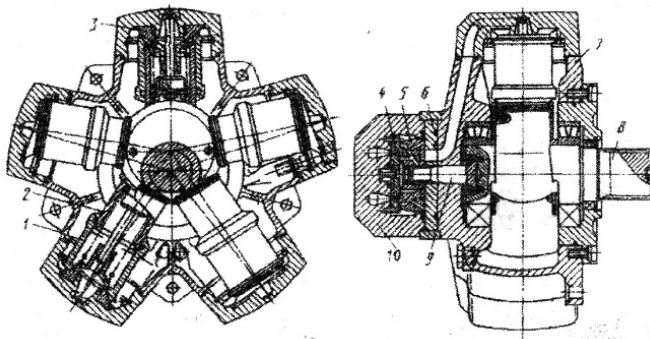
Высокомоментный радиально-поршневой гидромотор с качающимися цилиндрами
